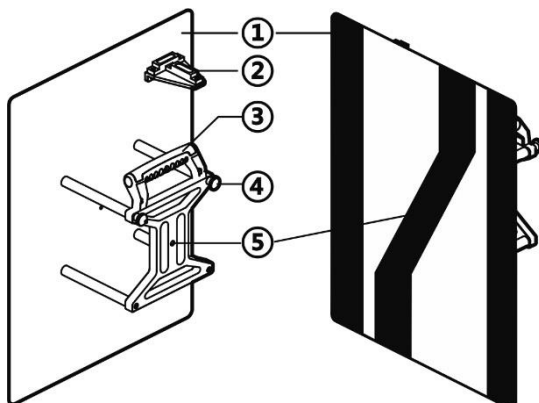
Калибровочная пластина радара, CSC0602/02
